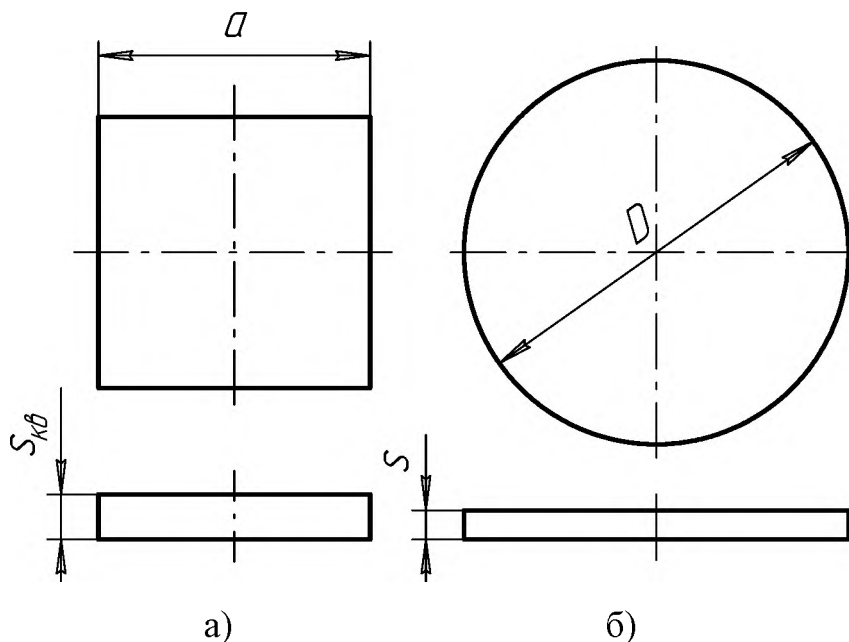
Заготовка (а) та деталь (б), що отримується процесом переформування квадратних заготовок у круглі
